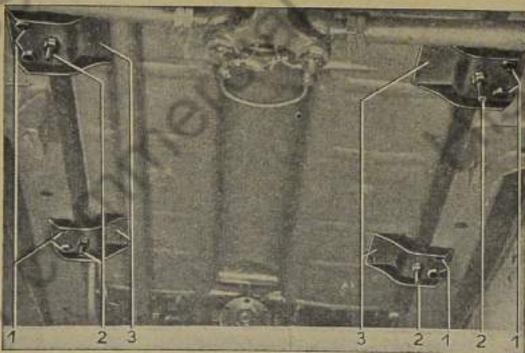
Tragarme für Kraftstoffbehälter abschrauben
